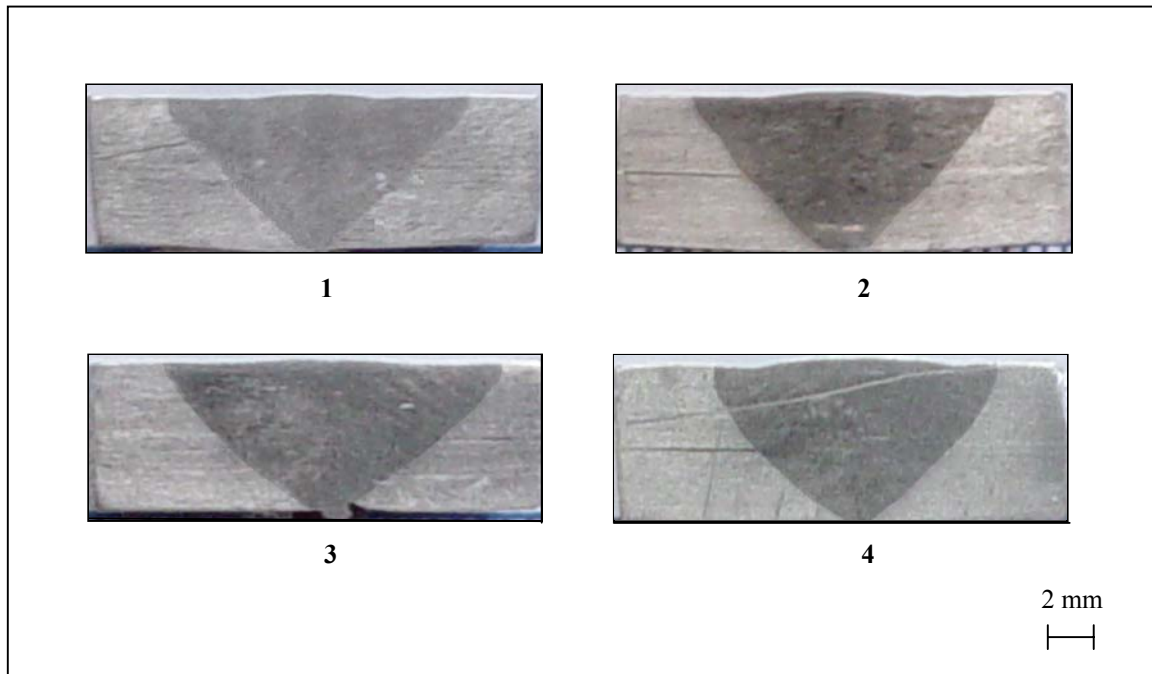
Macrografías de las cuatro condiciones de soldadura.
